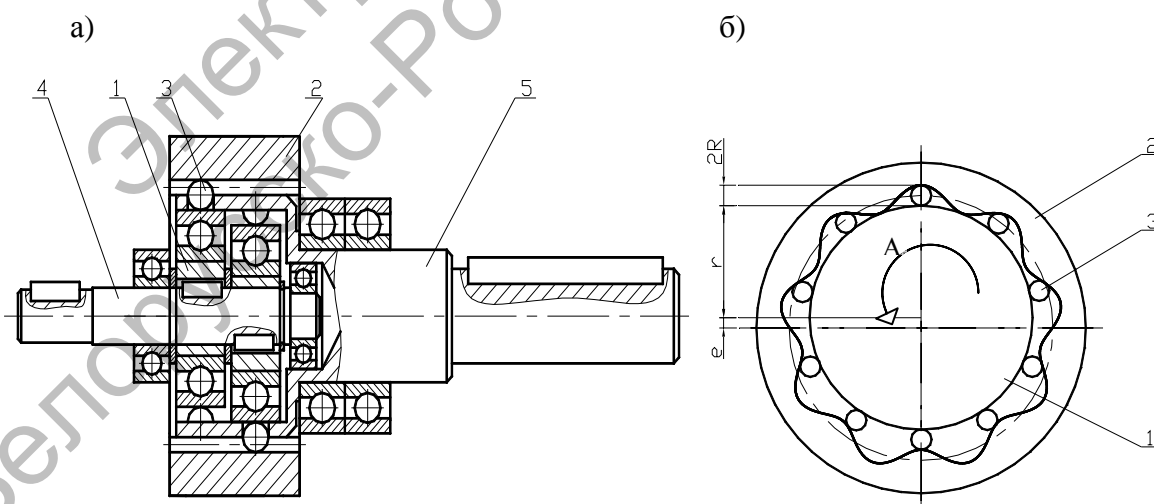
Конструктивная схема (а) и схема зацепления (б) шариковой радиально-плунжерной передачи
